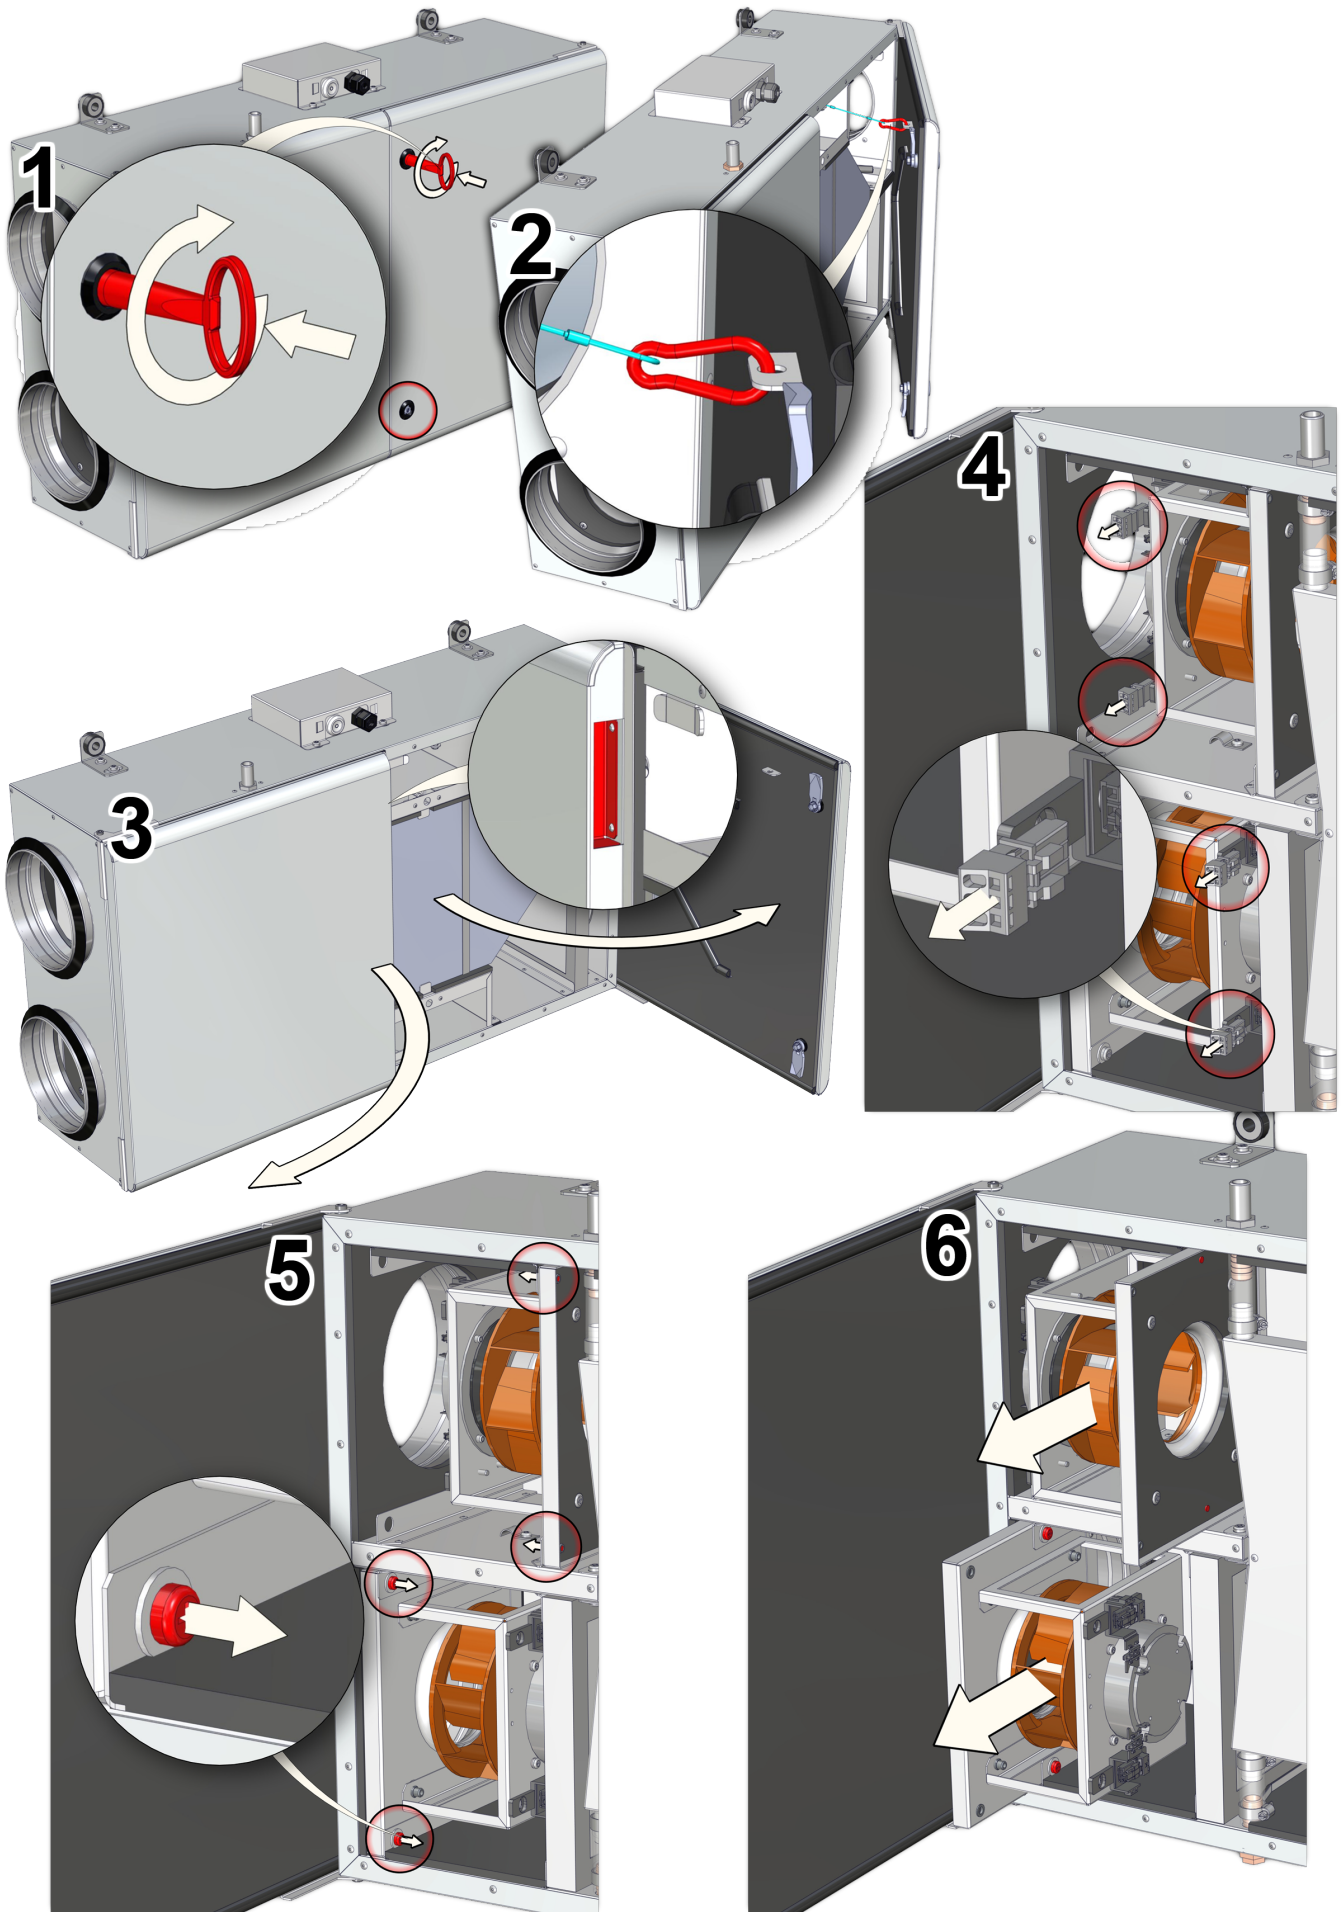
und 6: Die Baugruppe des Ventilators wird mit einer Hand gehalten und mit der zweiten Hand werden die Halteschrauben der Baugruppe abgeschraubt. (Auf solcher Weise den anderen Ventilator abschrauben.)
